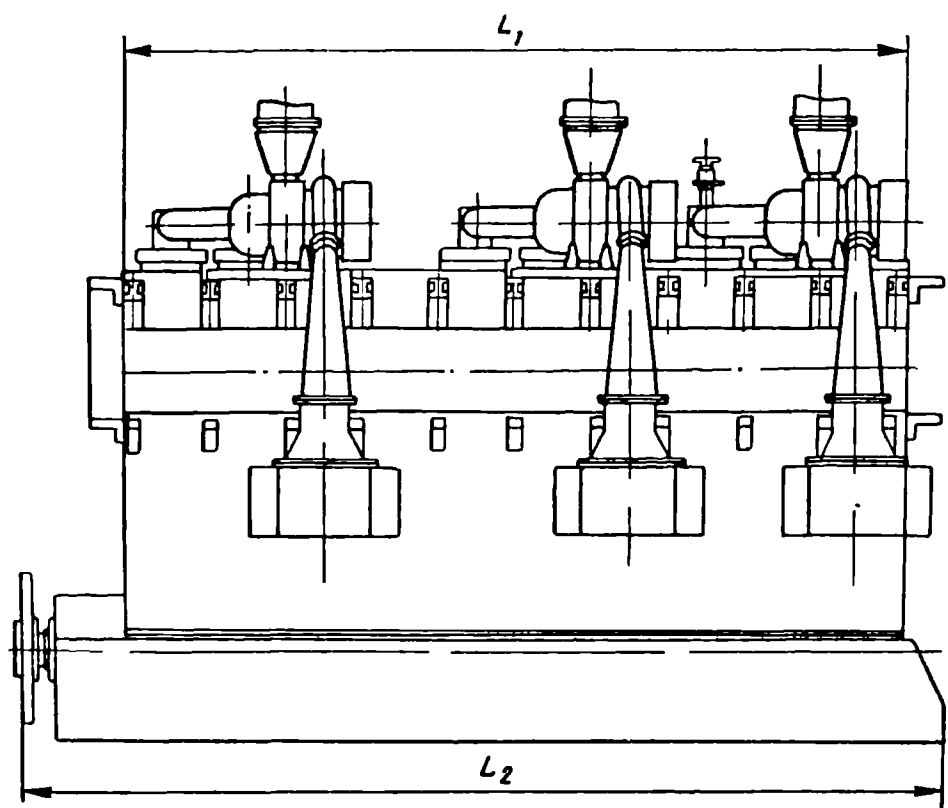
Габаритный чертеж двигателя 9ДКРН 80/160-4.
